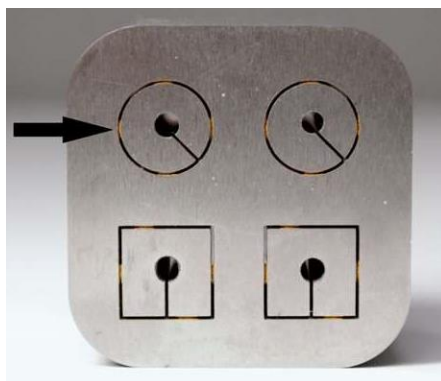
Elektródy používané pri EDM vrtaní [34].
